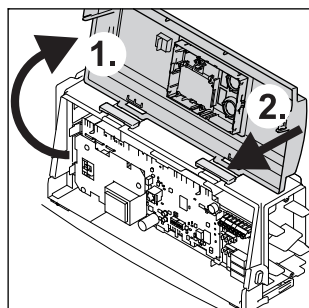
Frontblende öffnen und in Montageposition bringen.
